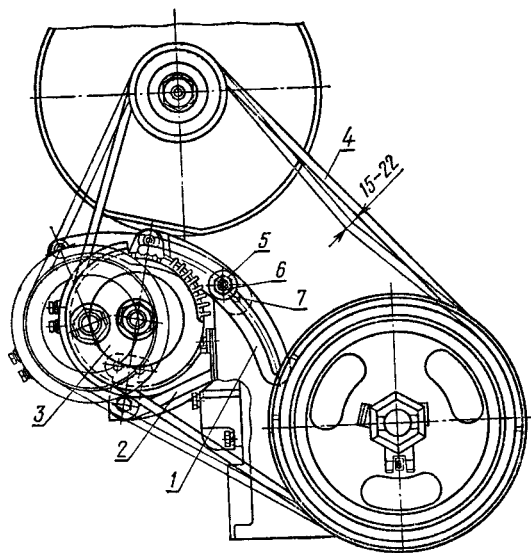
Устройство для натяжения ремней вентилятора дизеля Д-37Е:
